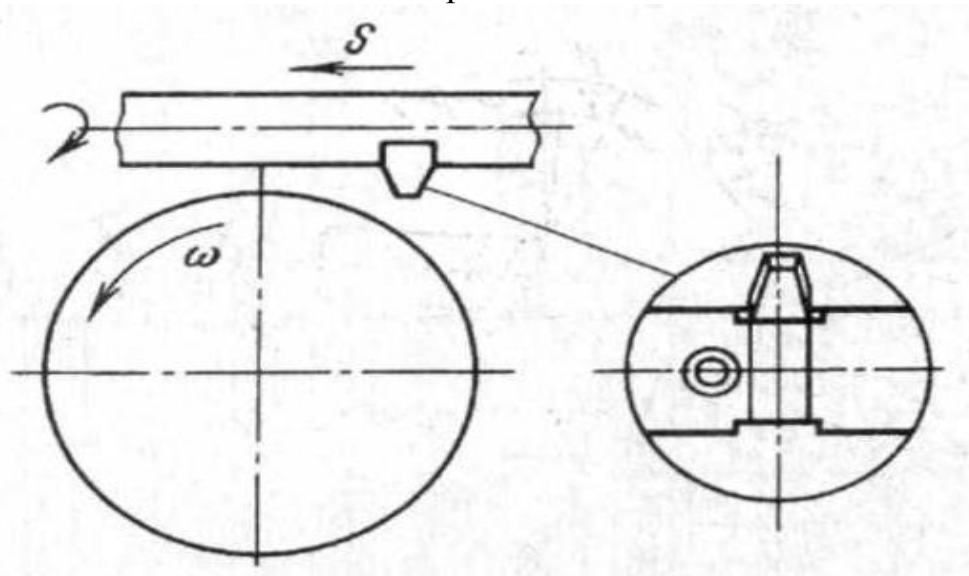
Схема нарезания червячного колеса однозубой фрезой.
